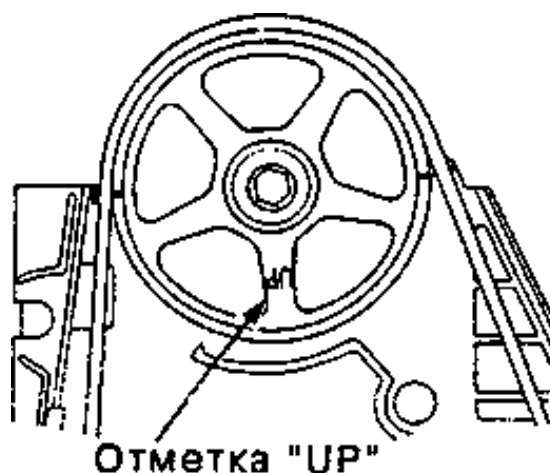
Положение шкива распредвала при регулировке клапанов четвёртого цилиндра
